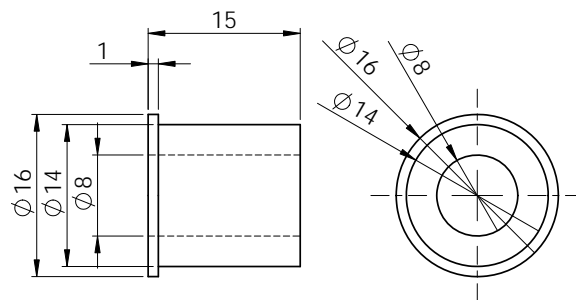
Technische Zeichnung des Strahlenschutzinsertes. Aus Messing gefertigt.
